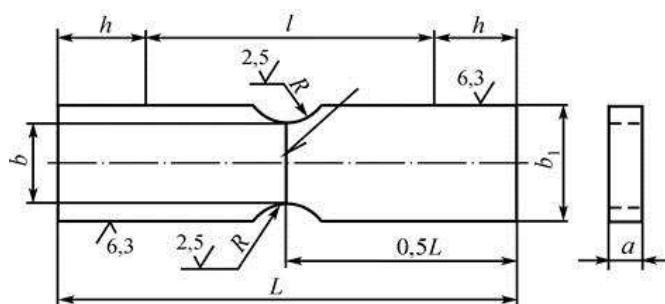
Образец для определения временного сопротивления металла шва
